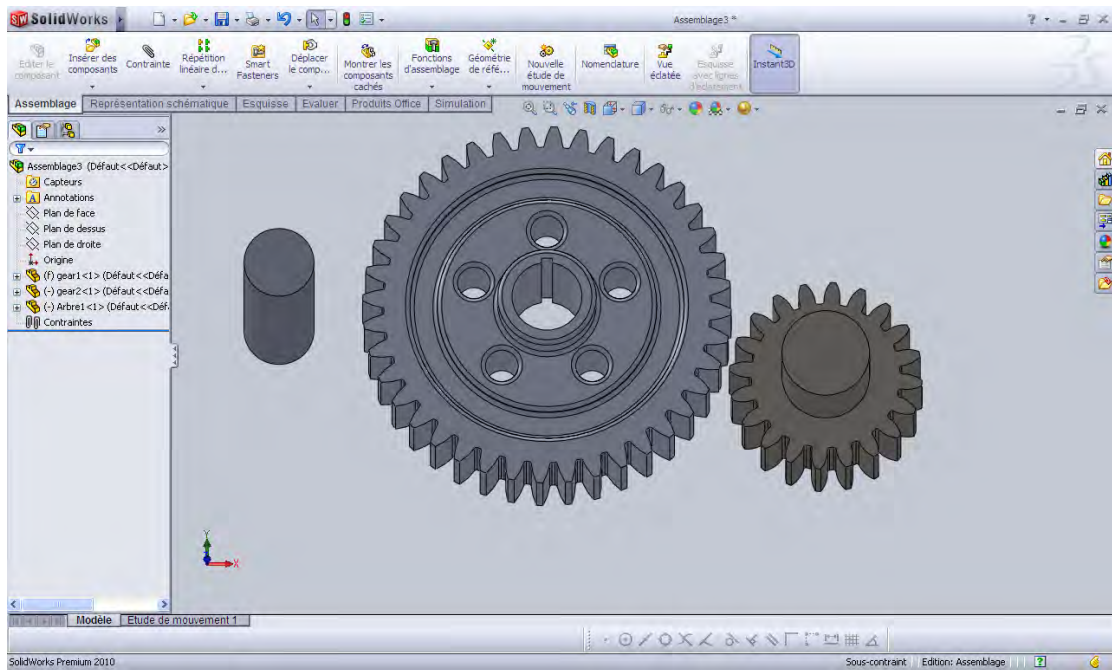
Première étape de construction de l'assemblage : importation des pièces
